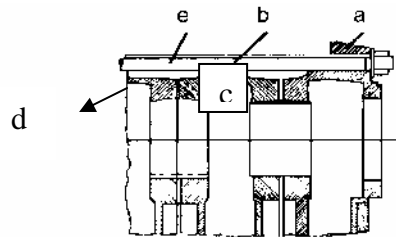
G Assemblage par nipples d'éléments de chaudière.
